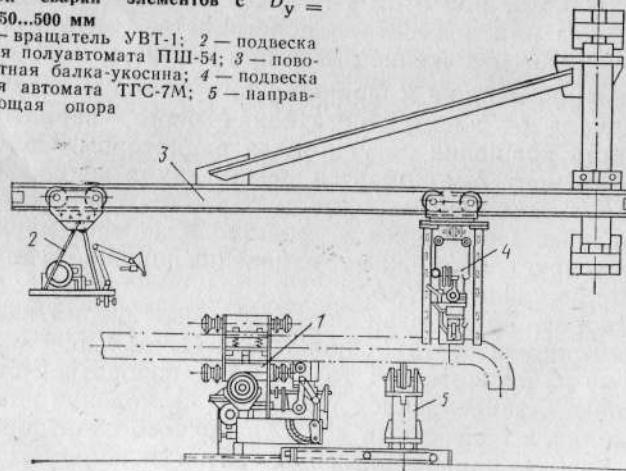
Пост для полуавтоматической сварки элементов с  $D_y = 50...500$  мм
